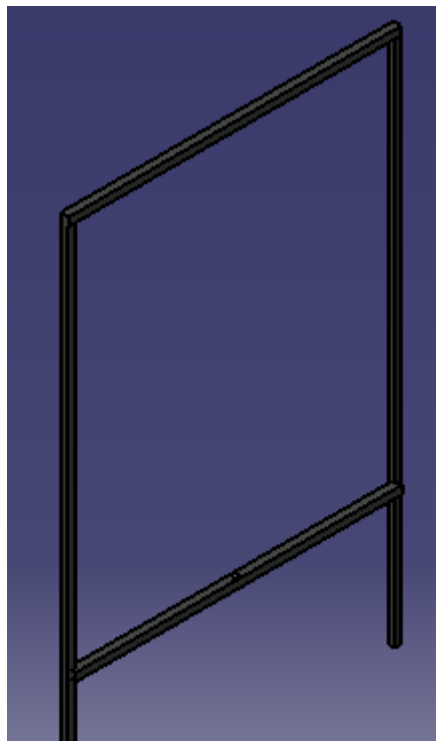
Diseño de la estructura de sujeción. Fuente: elaboración propia
